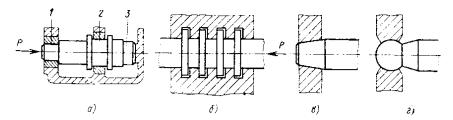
Опорные части валов и осей: а – цапфа; б – гребенчатая пята; в – конический шип; г – шаровой шип; 1 – шип; 2 – шейка; 3 – пята
